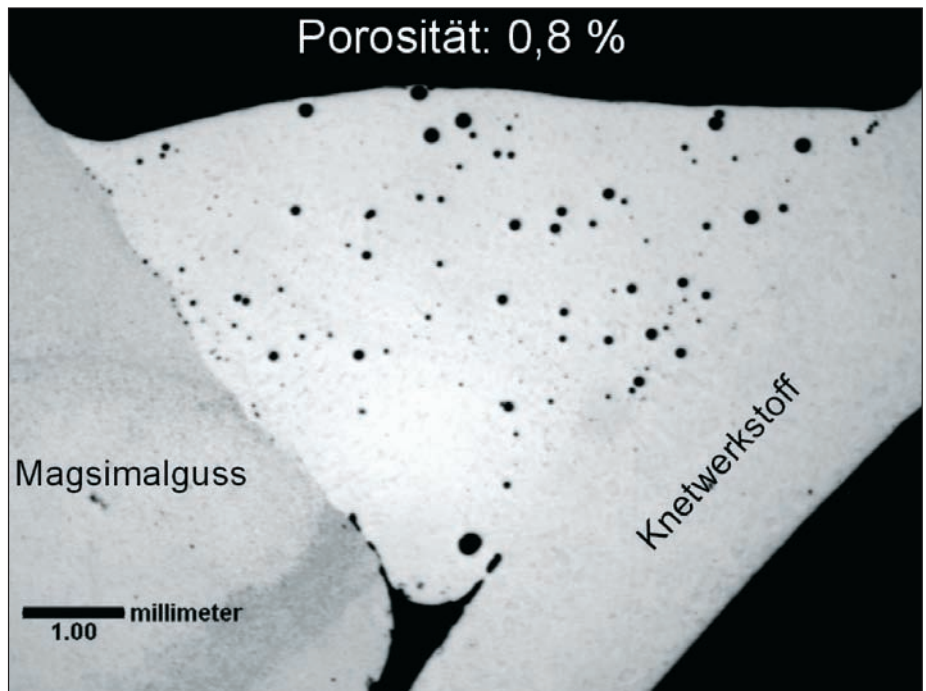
Metall-Inertgas-Schweißung (MIG) an einem Aluminiumdruckgussteil mit niedrigem Gasgehalt
